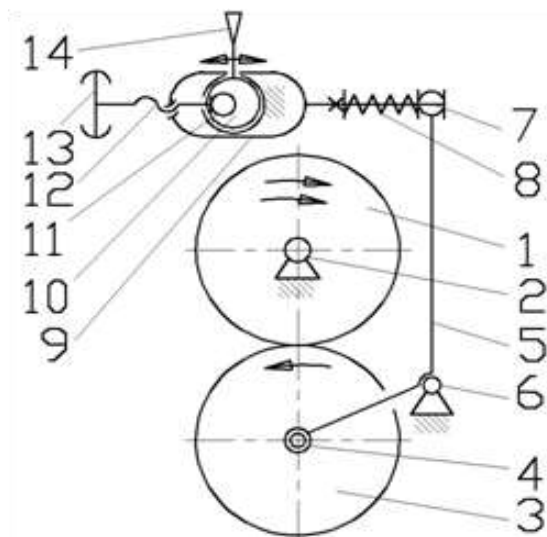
Схема вальцьового верстата.
